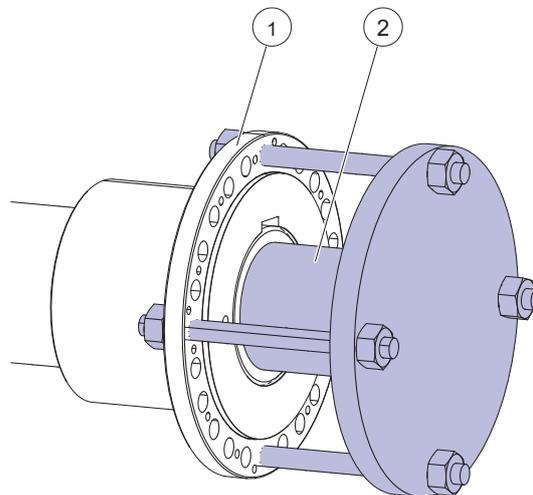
Presskörper festschrauben, Hydraulikaggregat anschließen
